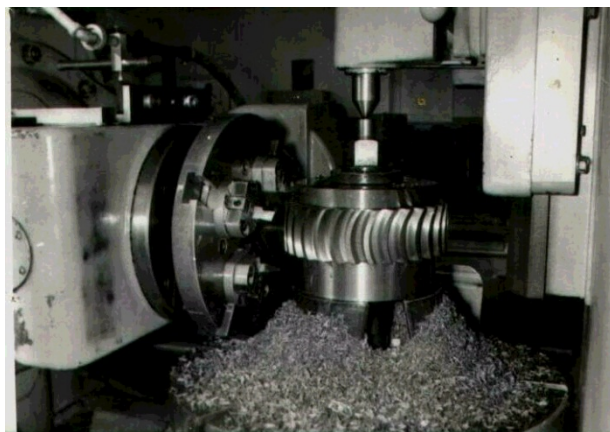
Зуборезный полуавтомат модели ЕСЗ 623.31
